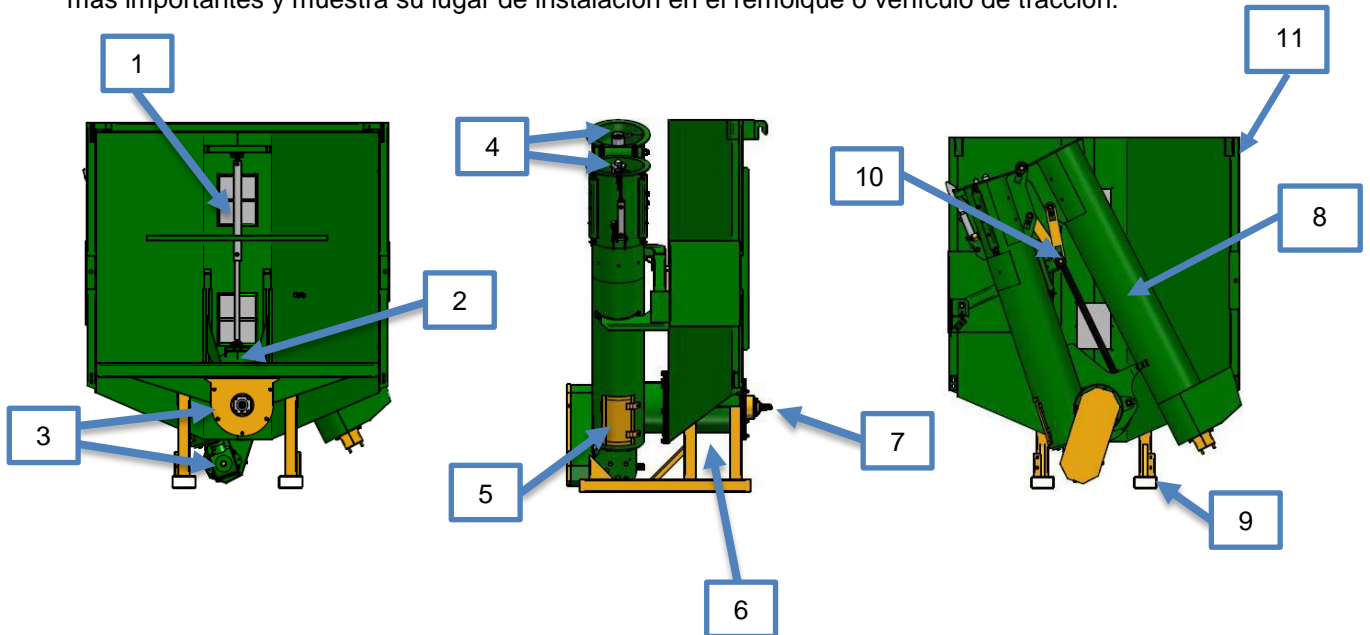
Componentes del sistema de transbordo por tornillo sinfín (Fig. ÜLS 400/500)
